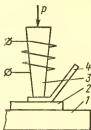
Схема термокомпрессионной сварки с подогревом инструмента:
